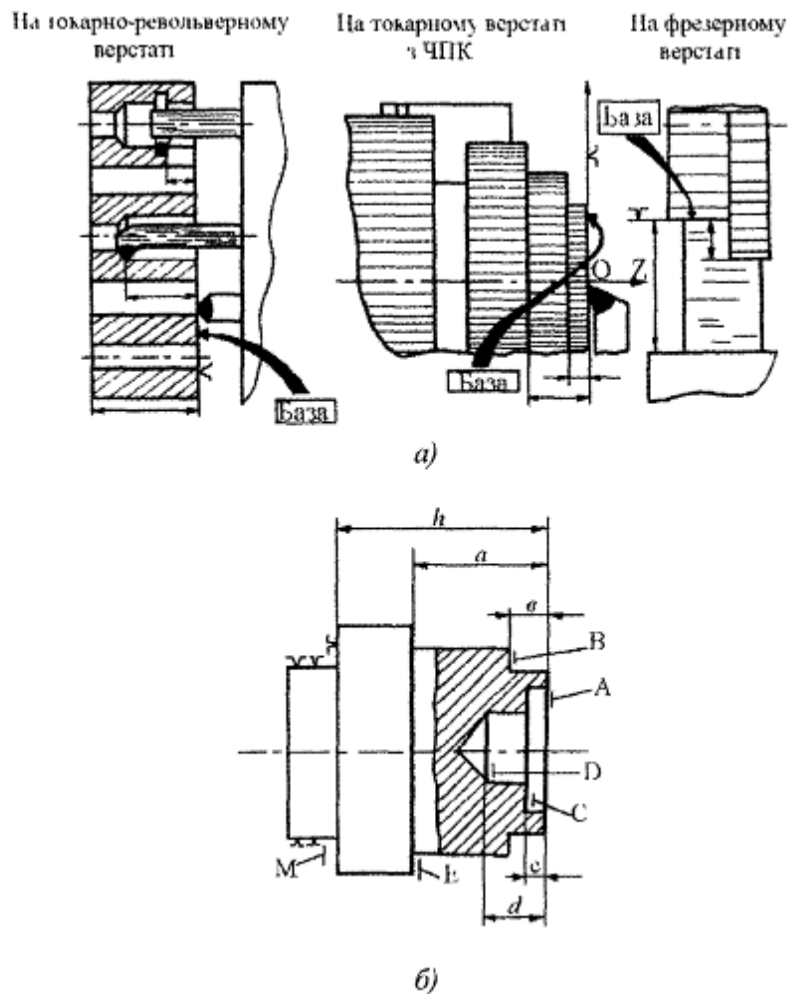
Настроювальні бази (а) та використання настрою вальної бази А при обробці заготовки на револьверному верстаті (б)
